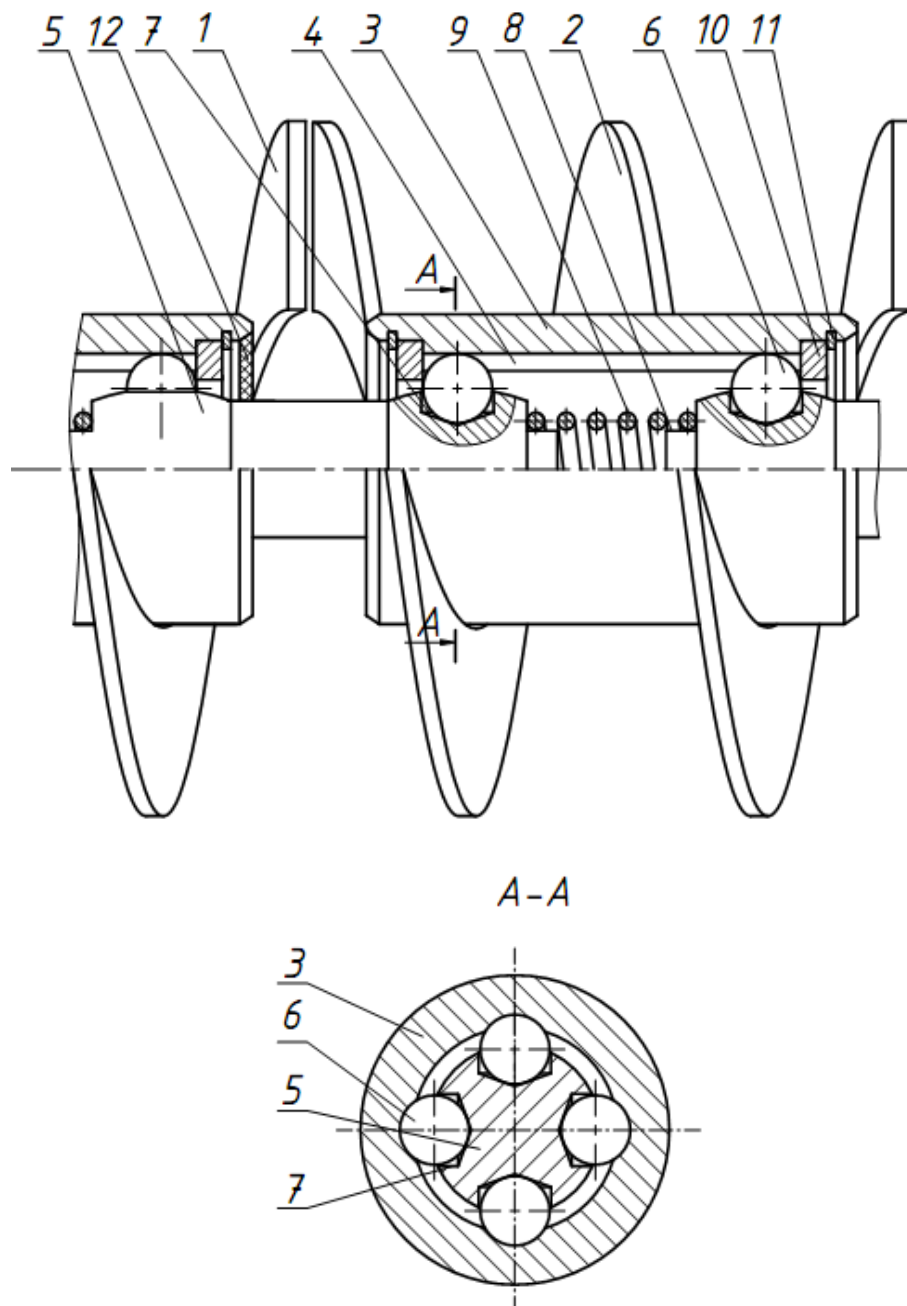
Конструктивна схема робочого органу гвинтового конвеєра [87]
